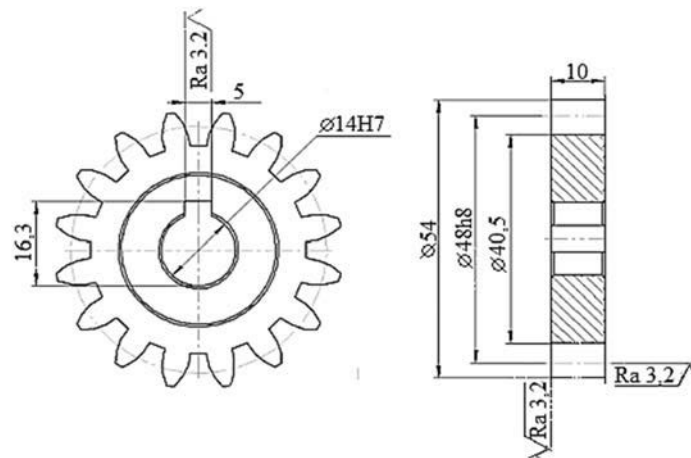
Деталь «Цилиндрическое зубчатое колесо»
